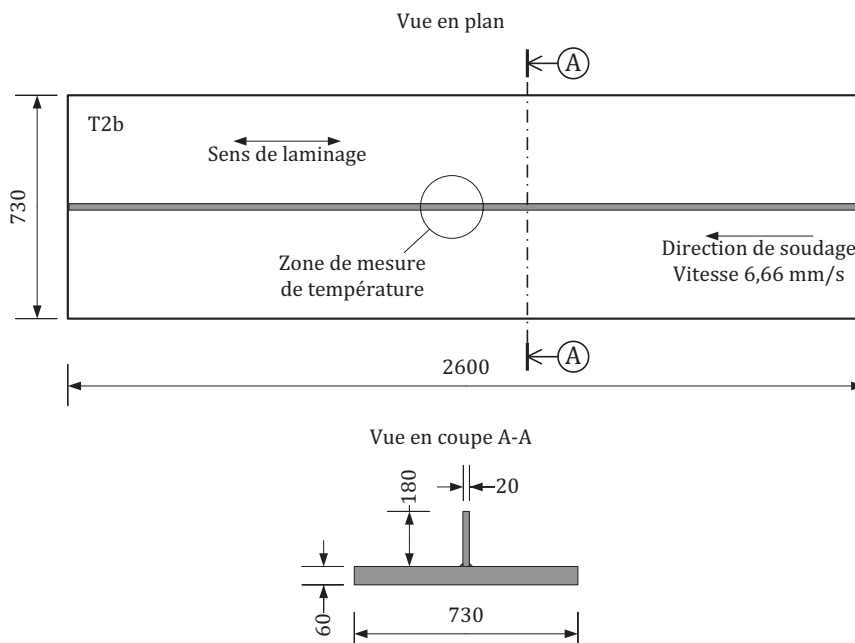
Vue en plan et coupe du soudage âme-semelle (dimensions en mm).
